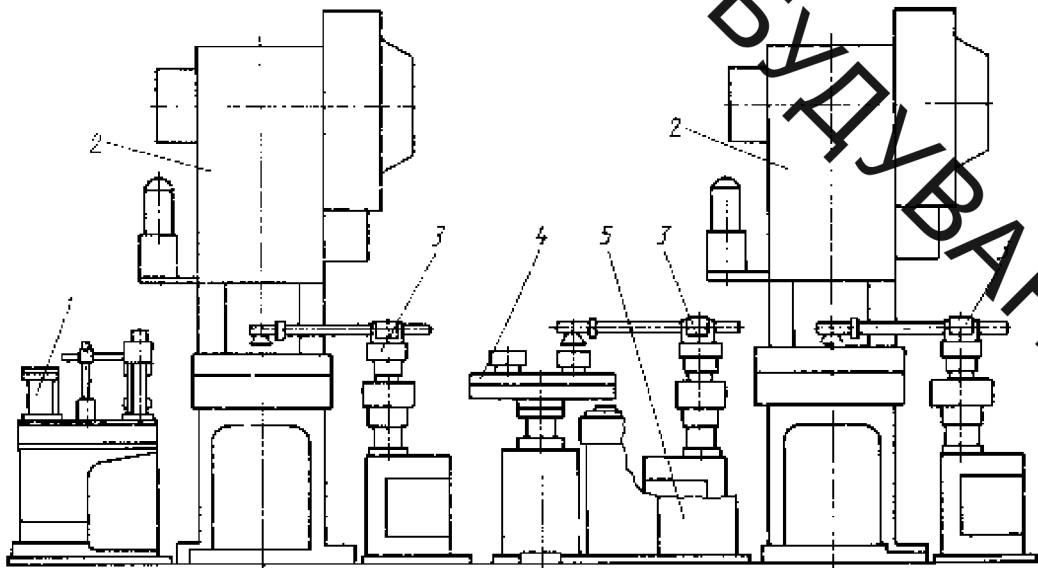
РТК для одно- і двохопераційного штампування на основі робота «Гном-32»
